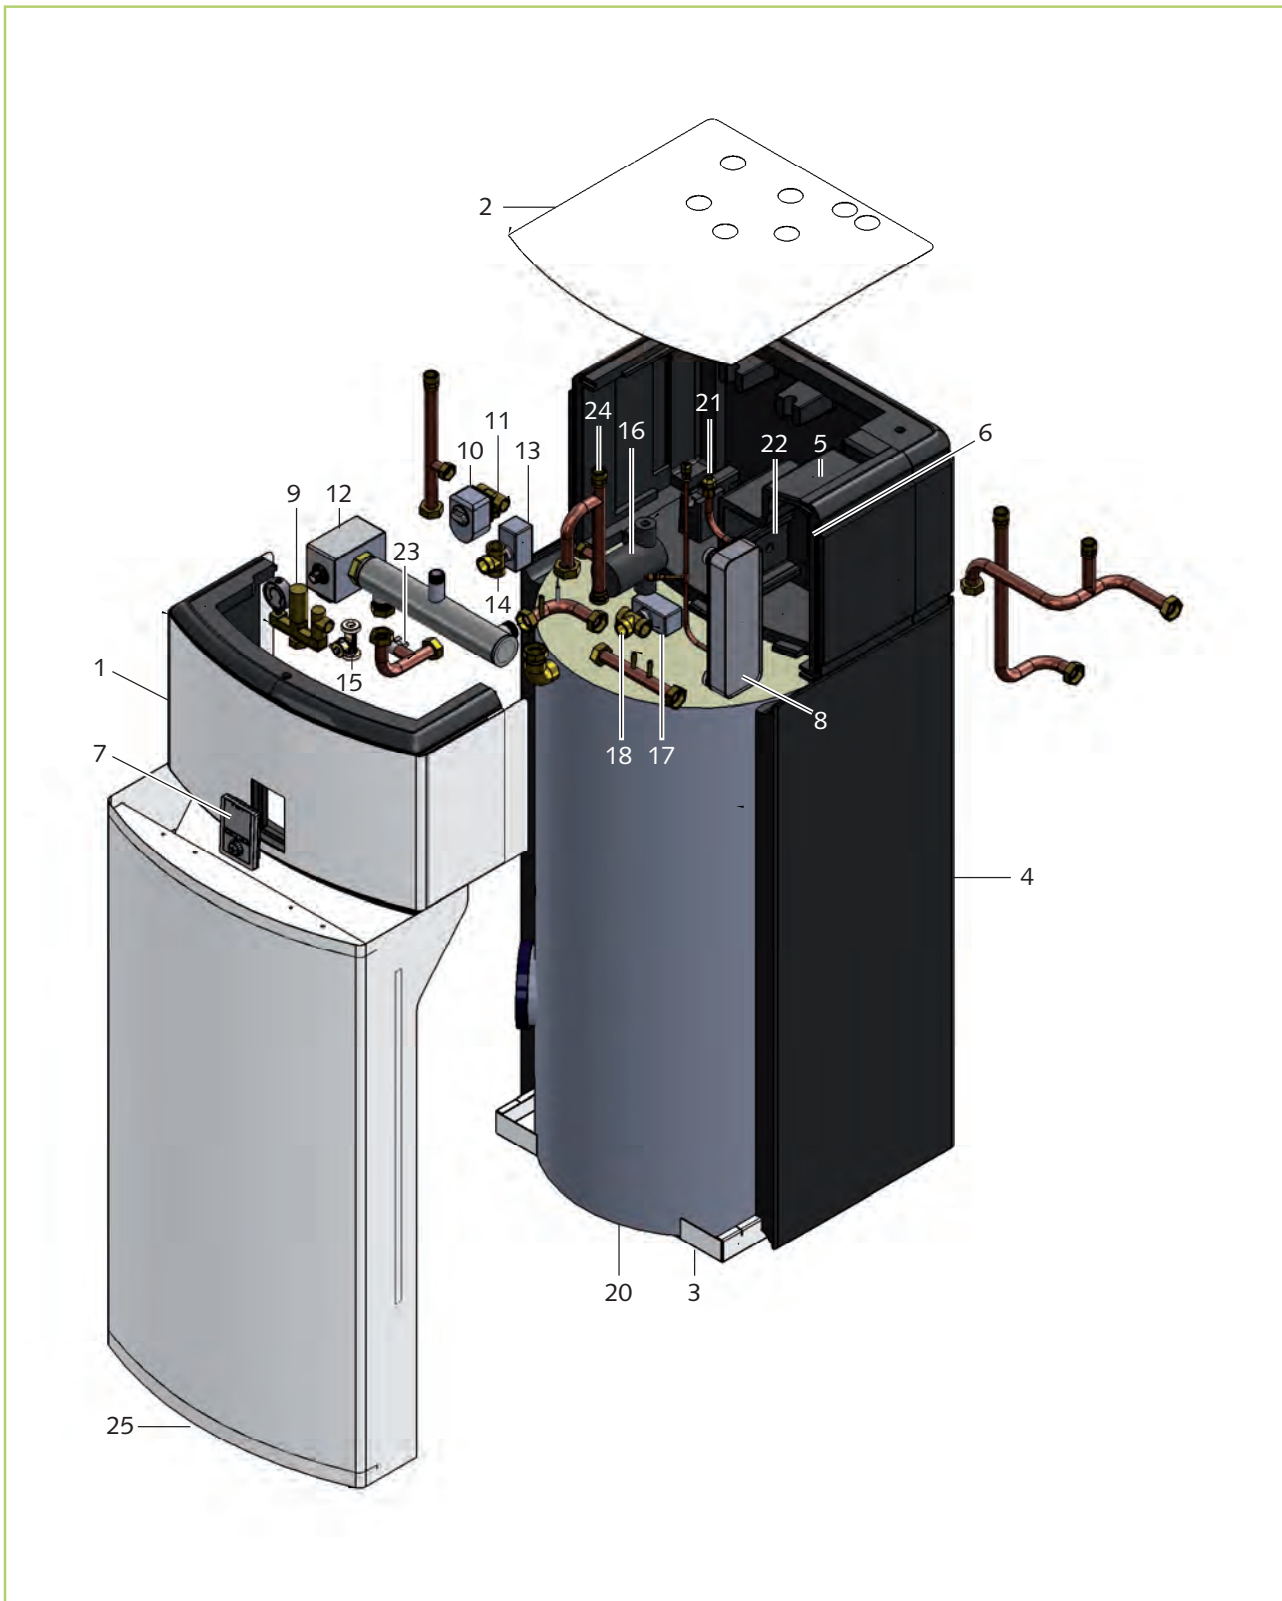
Explosionszeichnung Innenmodul WKF-compact 85/120/180
